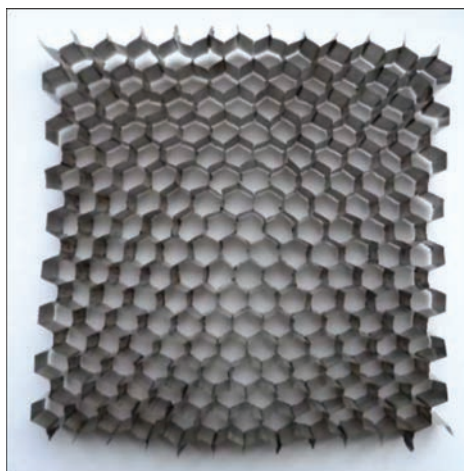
Сотовый заполнитель, изготовленный из фольги сплава ЮИПМ-1200
